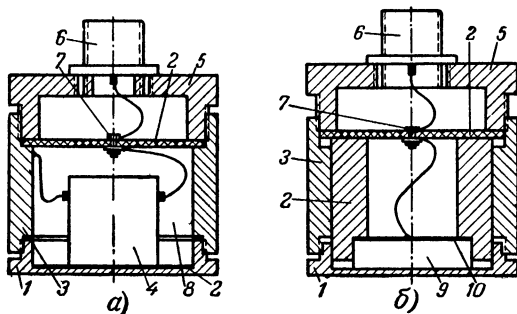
Схематический чертеж конструкции армировки пьезодатчиков из кристаллов сегнетовой соли и керамики титаната бария.
